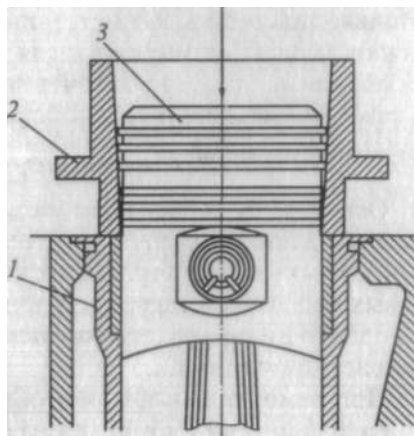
Установка поршня в сборе с шатуном в цилиндр: 1 - гильза блока цилиндров; 2 - оправка; 3 - поршень в сборе с кольцами и шатуном
